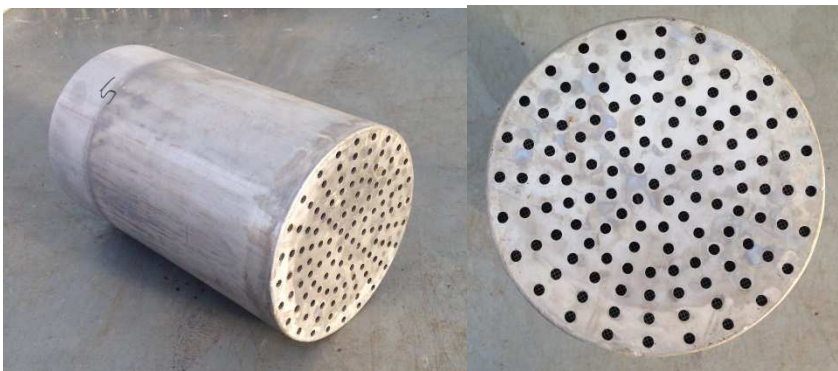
Photographie du cylindre de mesure. Vue d'ensemble (gauche), vue de la grille (droite)
